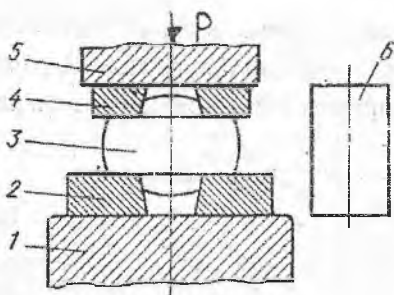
Схема осадки в подкладных кольцах: 1 - нижний боек, 2 - нижнее кольцо, 3 - заготовка после осадки, 4 - верхнее кольцо, 5 - верхний боек, 6 - заготовка
